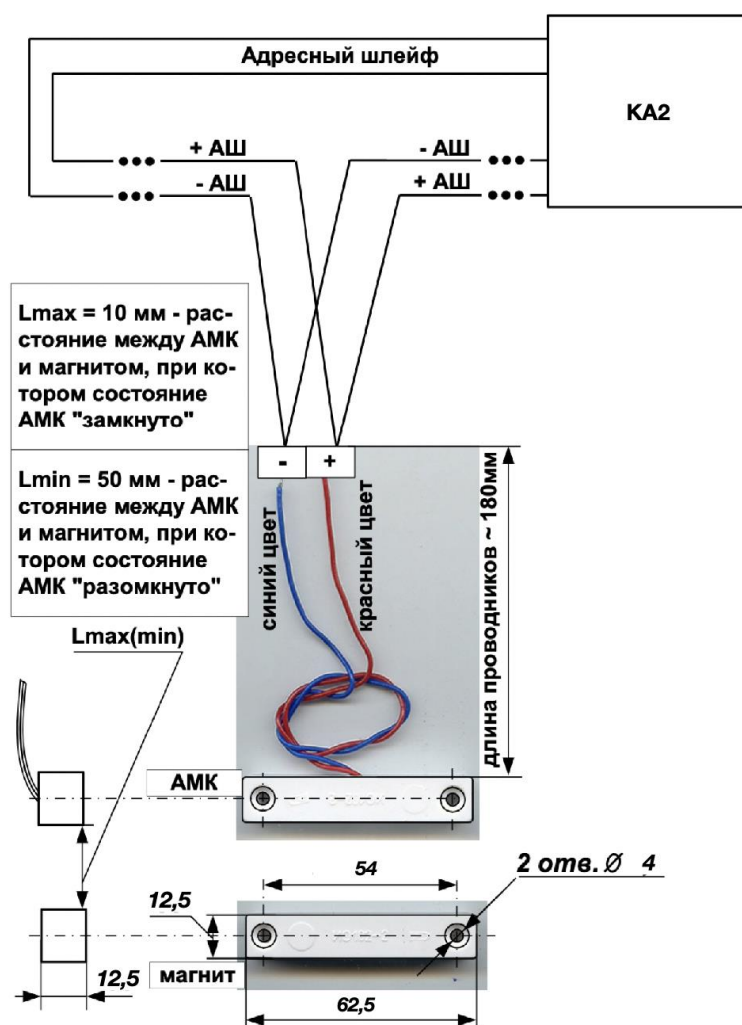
Конструкция, подключение, габаритные и присоединительные размеры
